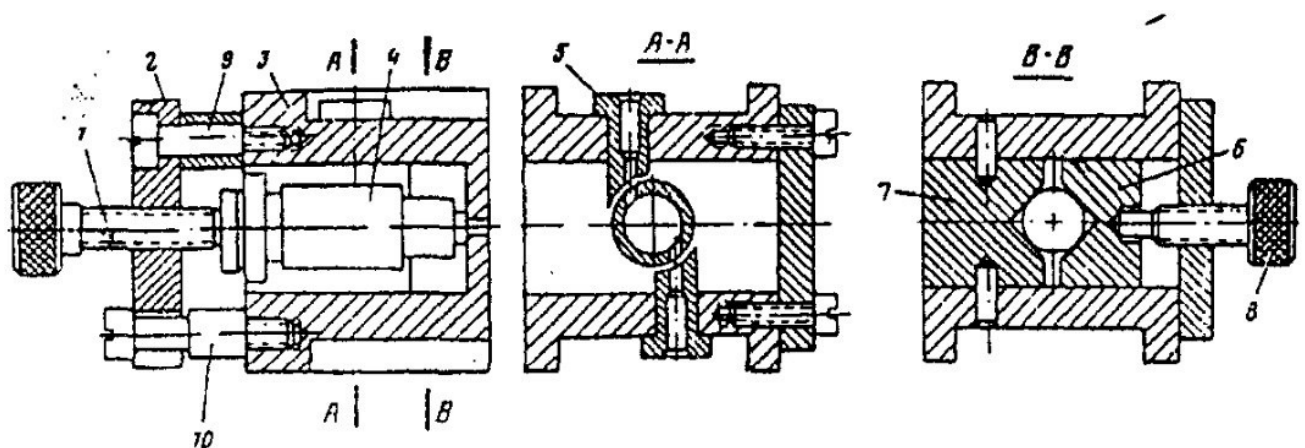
Кондуктор для свердління тангенціальних каналів:
